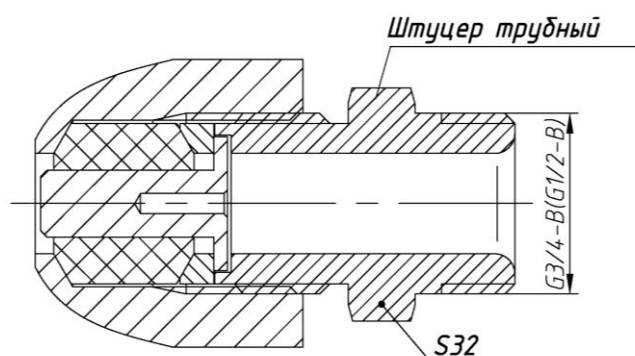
Элементы кабельного ввода для прокладки кабеля в трубе. Остальное см.
